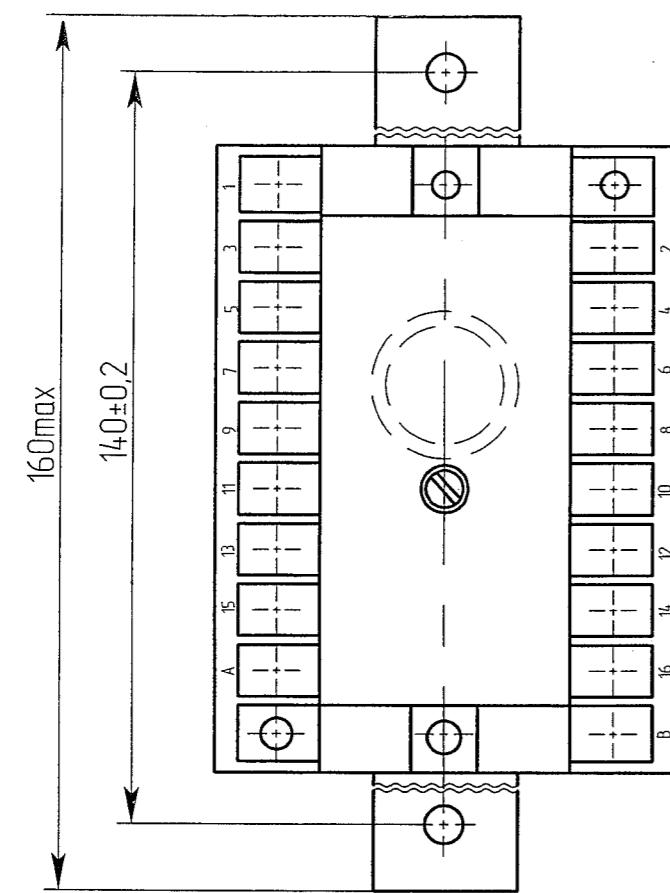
Реле типов PCB18-11-P-XXXX1, PCB18-12-P-XXXX1, PCB18-11-P-XXXX2, PCB18-12-P-XXXX2. Остальное см. рисунок Б.1
